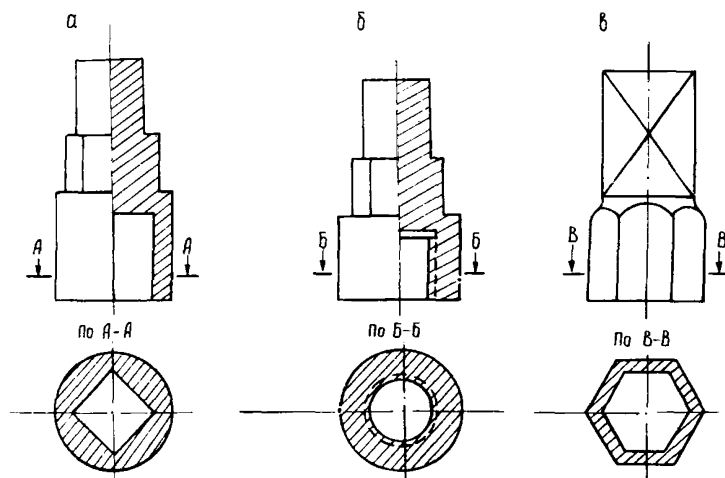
Насадки к сверлу для вращения стержня анкера при:
